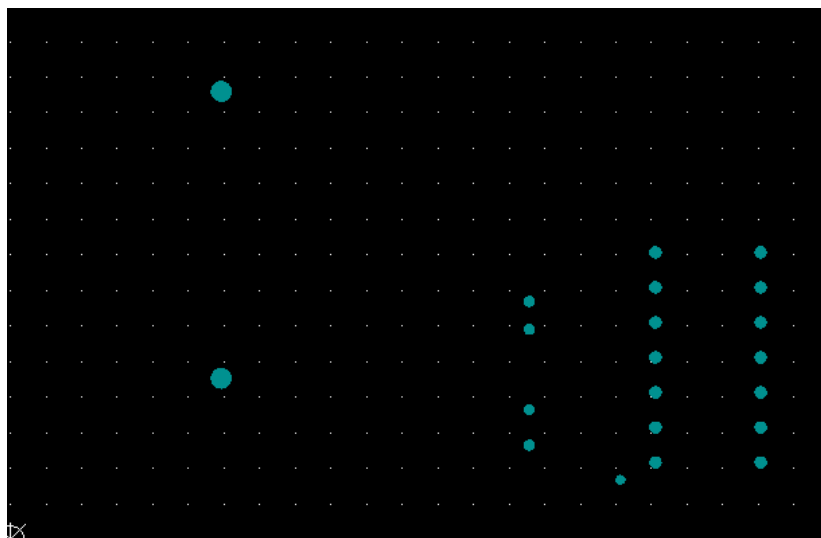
Готовый файл сверловки сквозных отверстий
